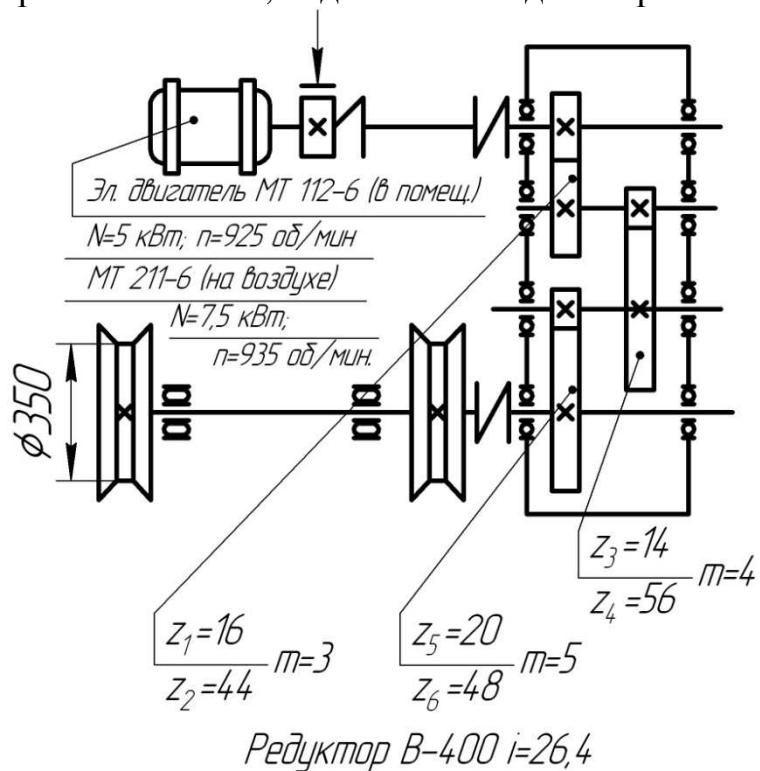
Кинематическая схема механизма передвижения грузовой тележки крана
